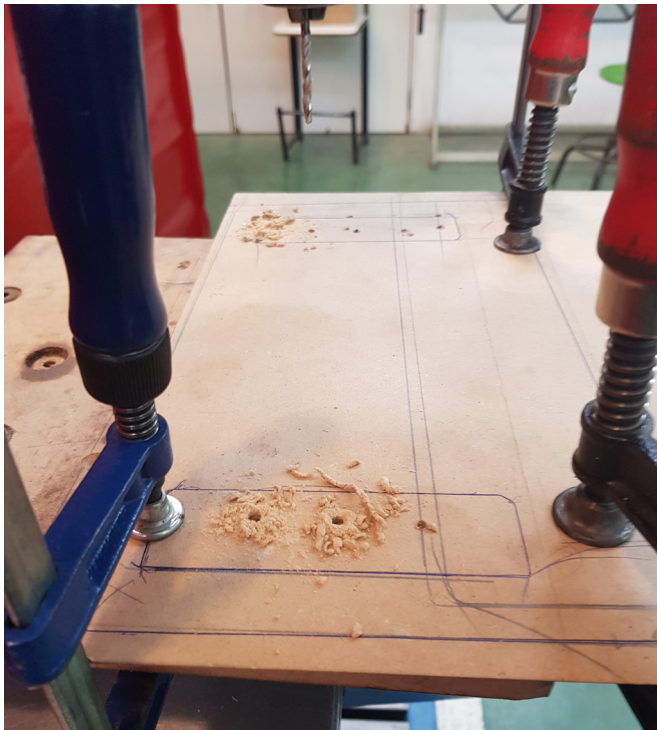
e Fig. 47 - Corte e furação das placas de MDF para construir a caixa.
